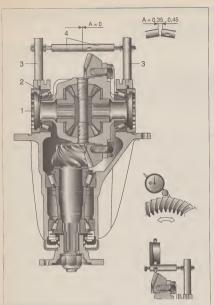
Приспособление для контроля предварительного натяга подшилников дифференциала: 1 — регулировочная гайка; 2 — подшилник; 3 — стойка приспособления; 4 — стержни.
